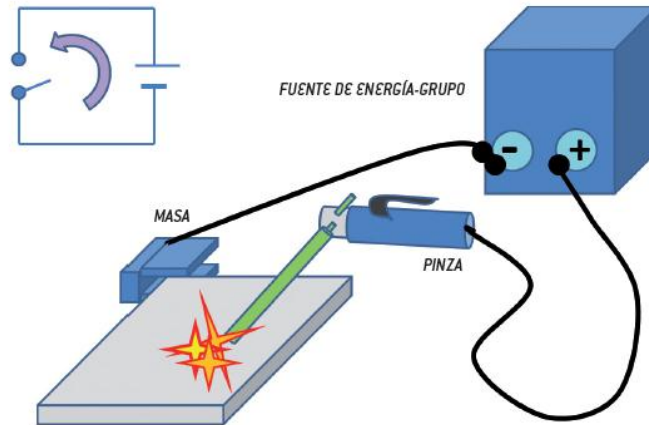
19: Proceso del sistema de soldadura de arco manual.
